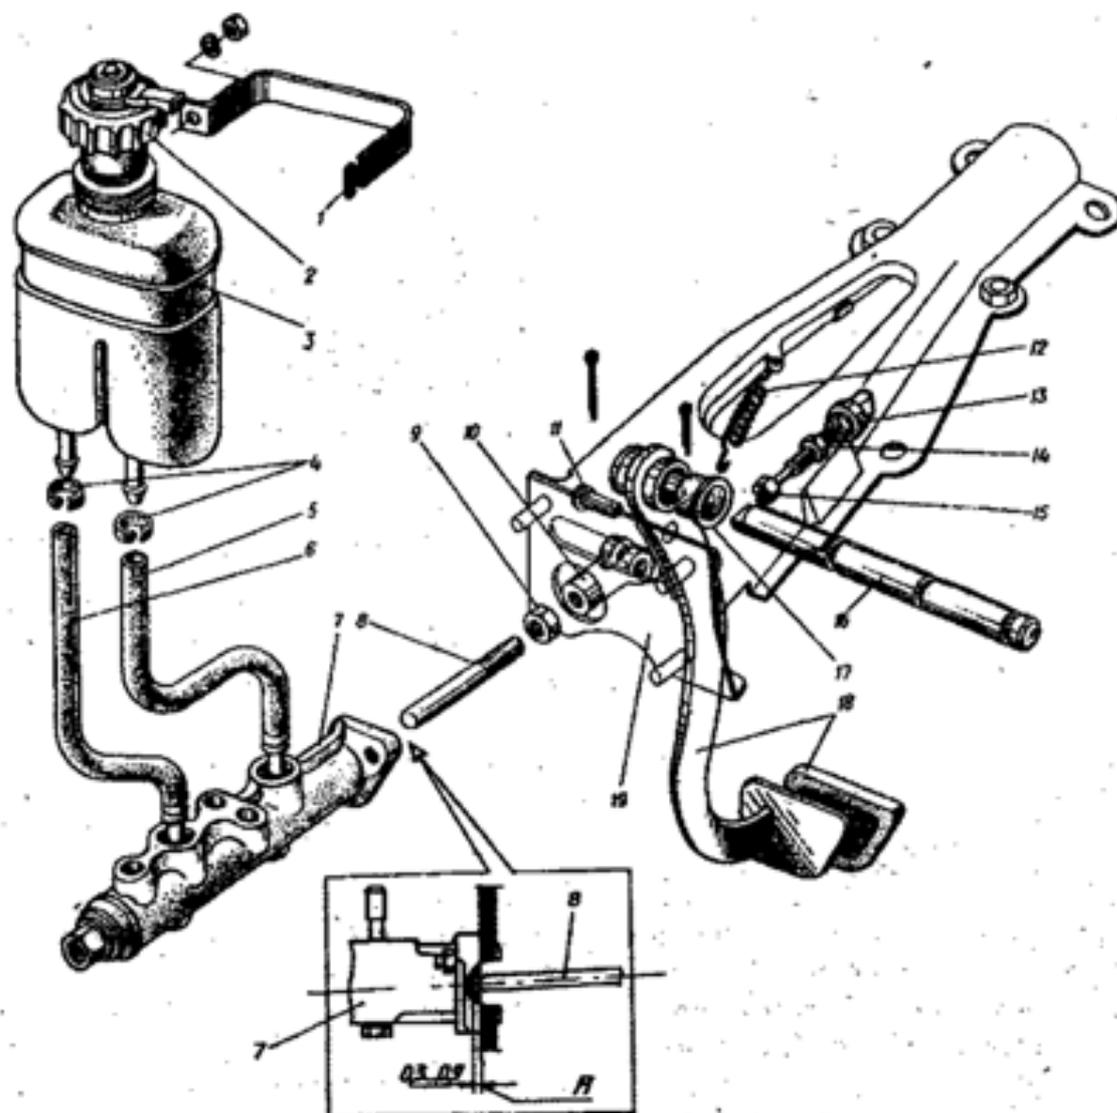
Гидропривод тормоза ножного: 1 - прижим бачка; 2 - датчик уровня жидкости; 3 - бачок; 4 - хомут; 5 - шланг передней полости; 6 - шланг задней полости; 7 - цилиндр главный; 8 - толкатель поршня; 9, 14 - контргайка; 10 - вилка толкателя; 11 - палец; 12 - пружина возвратная; 13 - включатель стоп-сигнала; 15 - наконечник; 16 - ось педалей; 17 - втулка педали; 18 - педаль; 19 - кронштейн педалей.
